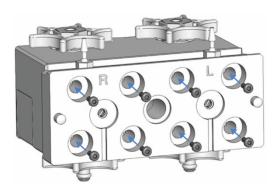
Pumpenkopf mit Hinterspülplatte und Schrauben für die Platte
